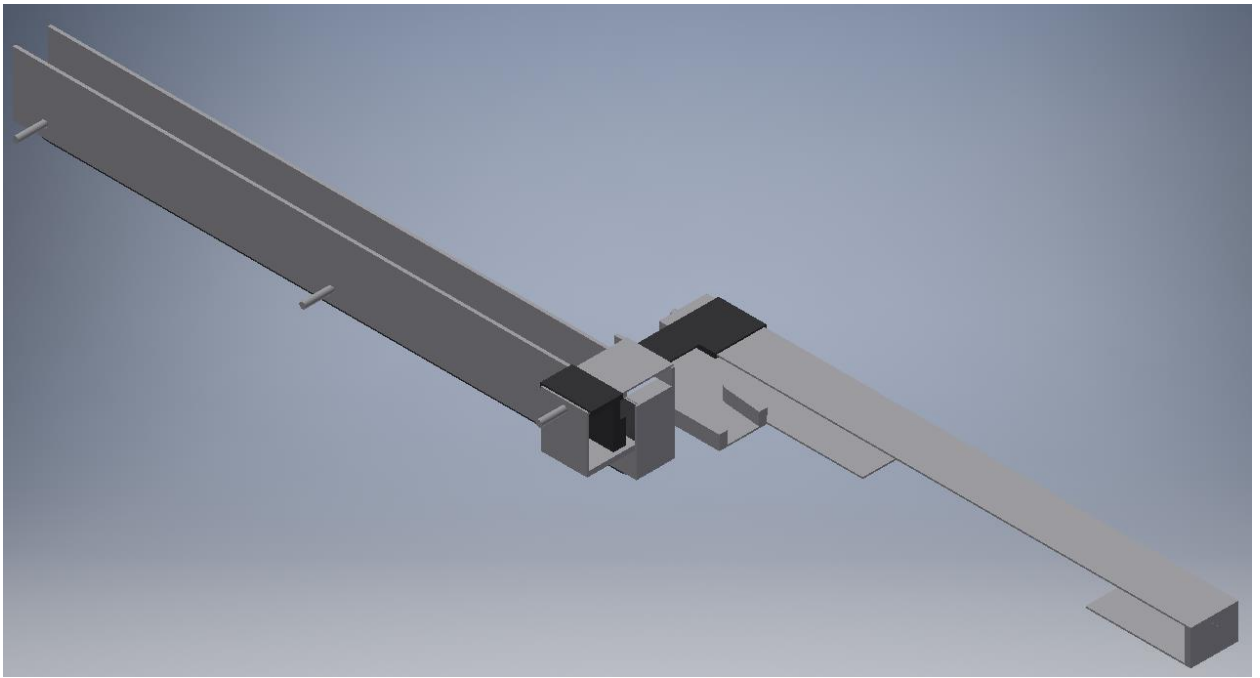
Модель сборки ленточного конвейера с толкателями
